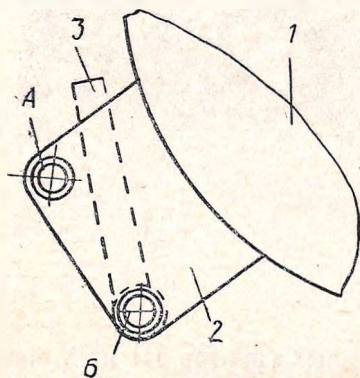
Заслонка ковша скрепера ДЗ-149-5:
